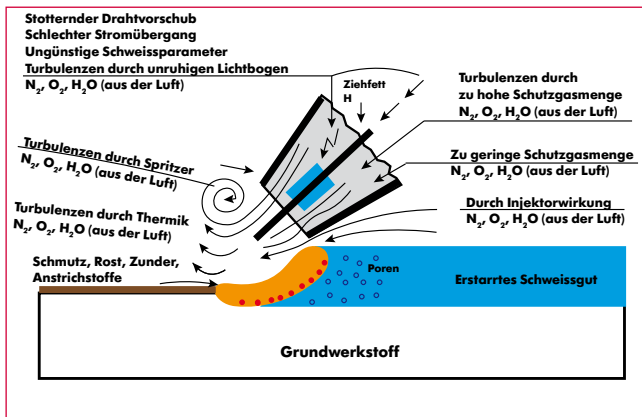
Störeinflüsse beim MSG-Schweißen
